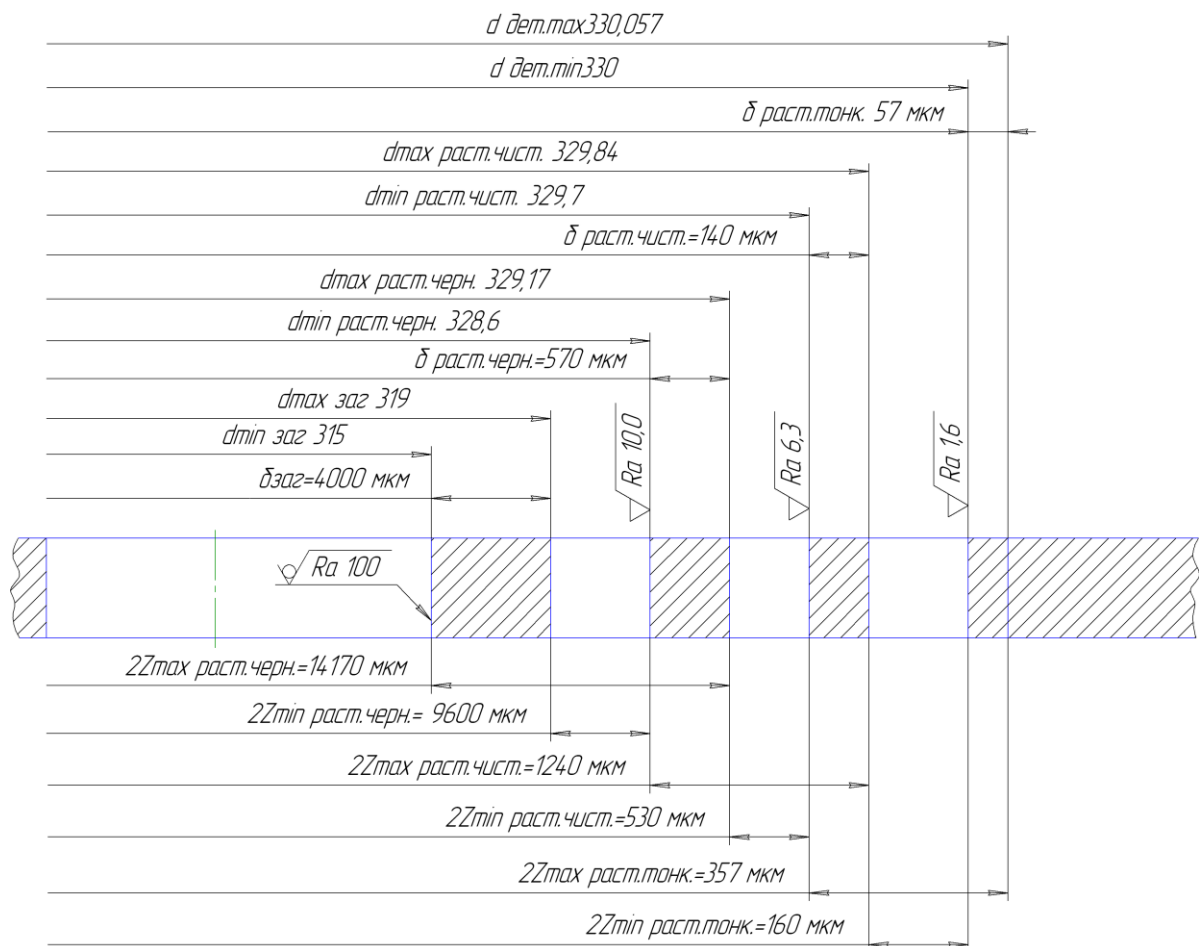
Схема розташування полів припусків і допусків на розмір
